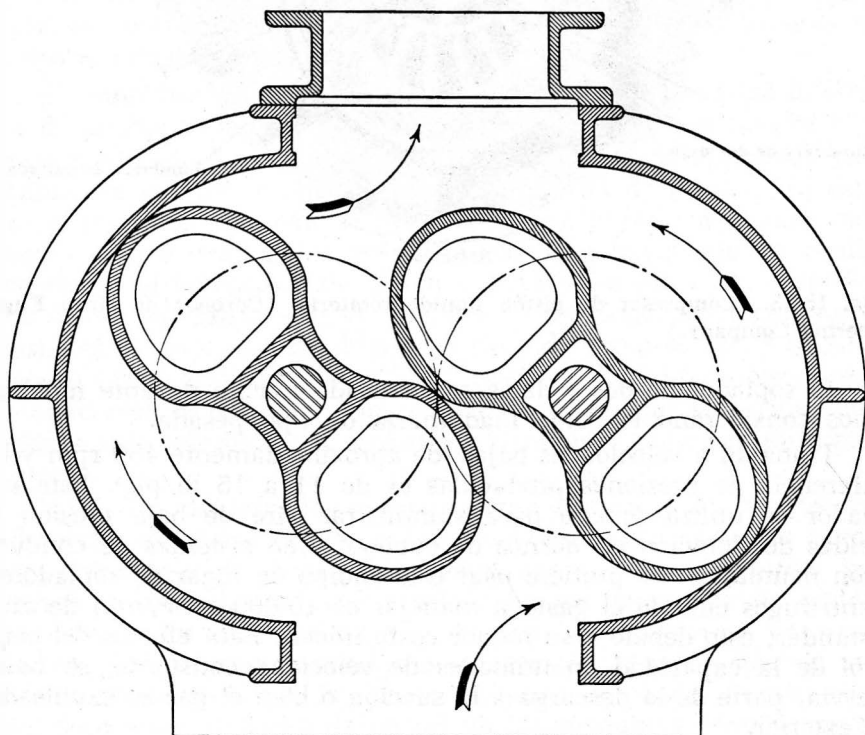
Soplador de dos rodetes. (Cortesía de Roots-Connersville Blower Division of Dresser Industries.)
